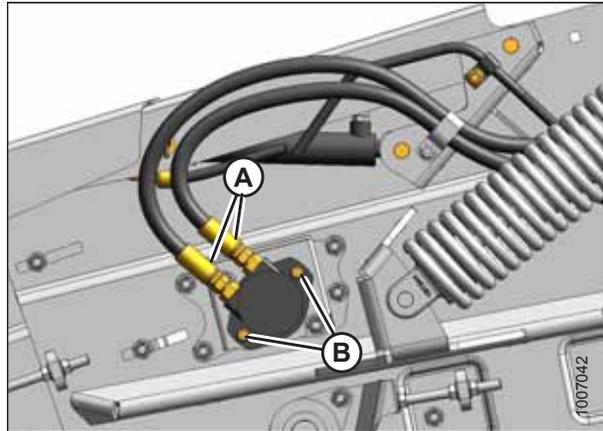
Motor hidráulico frontal – lado esquerdo
